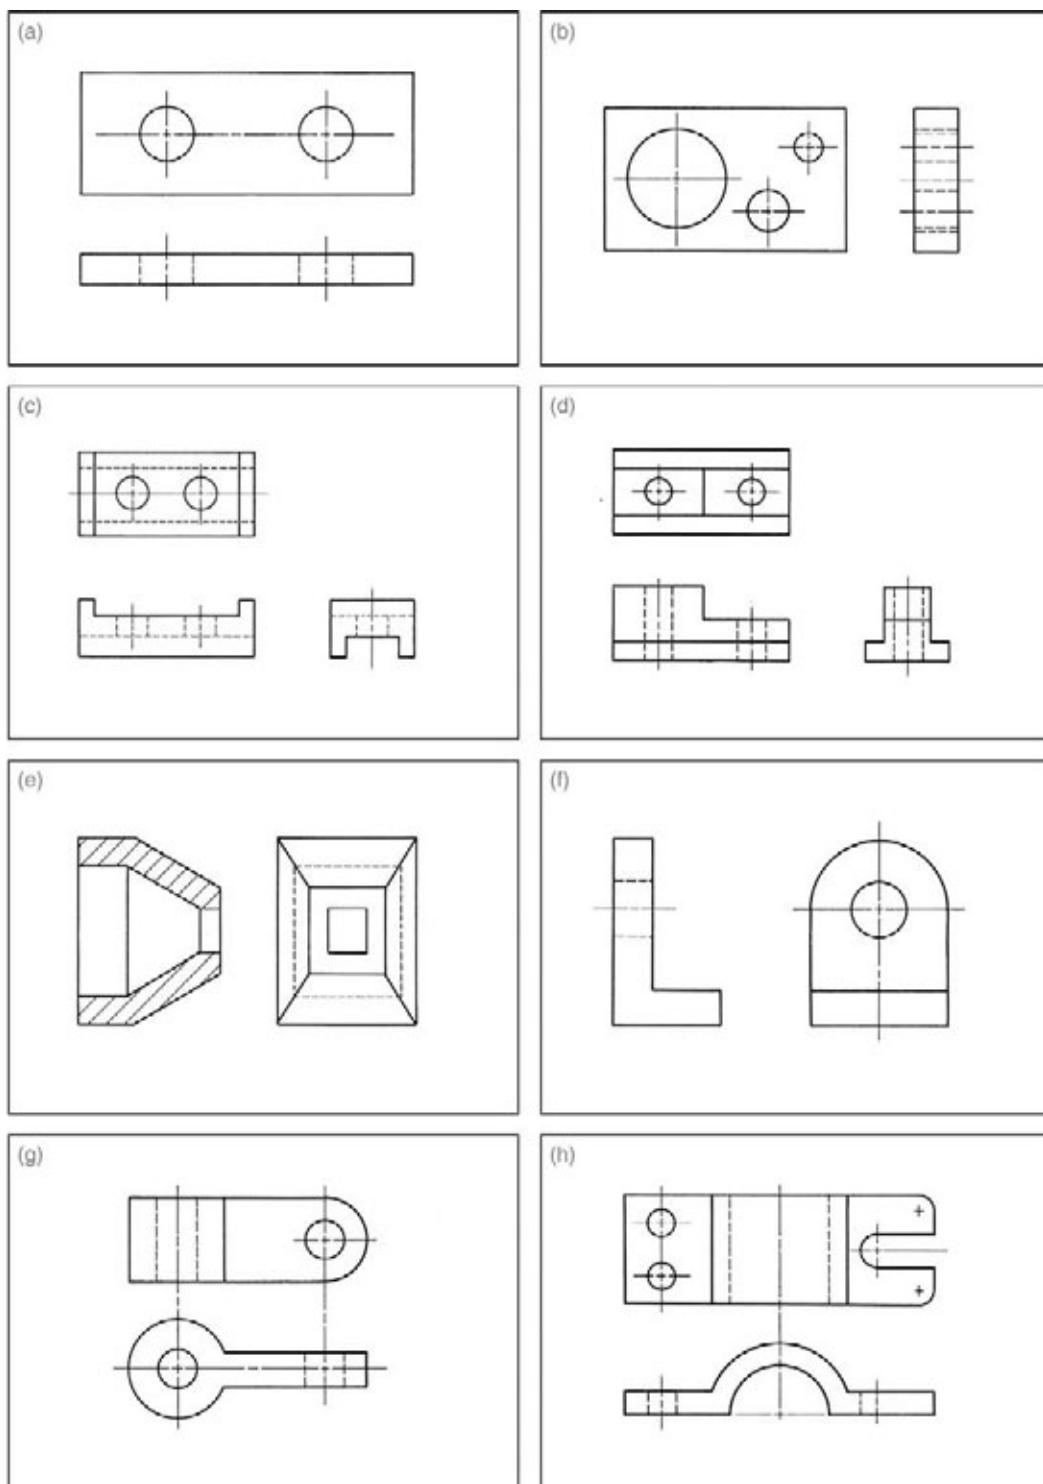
Utilice el esquema A-3 o A4-3 (ajustado), bosqueje o use CAD para dibujar las partes mostradas. Para determinar tamaños, haga dimensiones de la figura. Suponga que las partes se muestran aquí a la mitad de su tamaño. Según se asigne, dimensione el dibujo por completo con una cifra decimal para los milímetros o dos cifras decimales para las pulgadas, a tamaño completo. Para ver equivalencias de décimas de pulgada y milímetros, consulte la tercera de forros.
